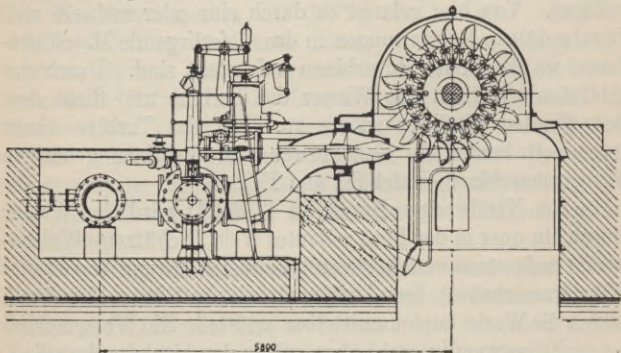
Eine Pelton-turbine im Gehäuse mit Düse und Regler.
